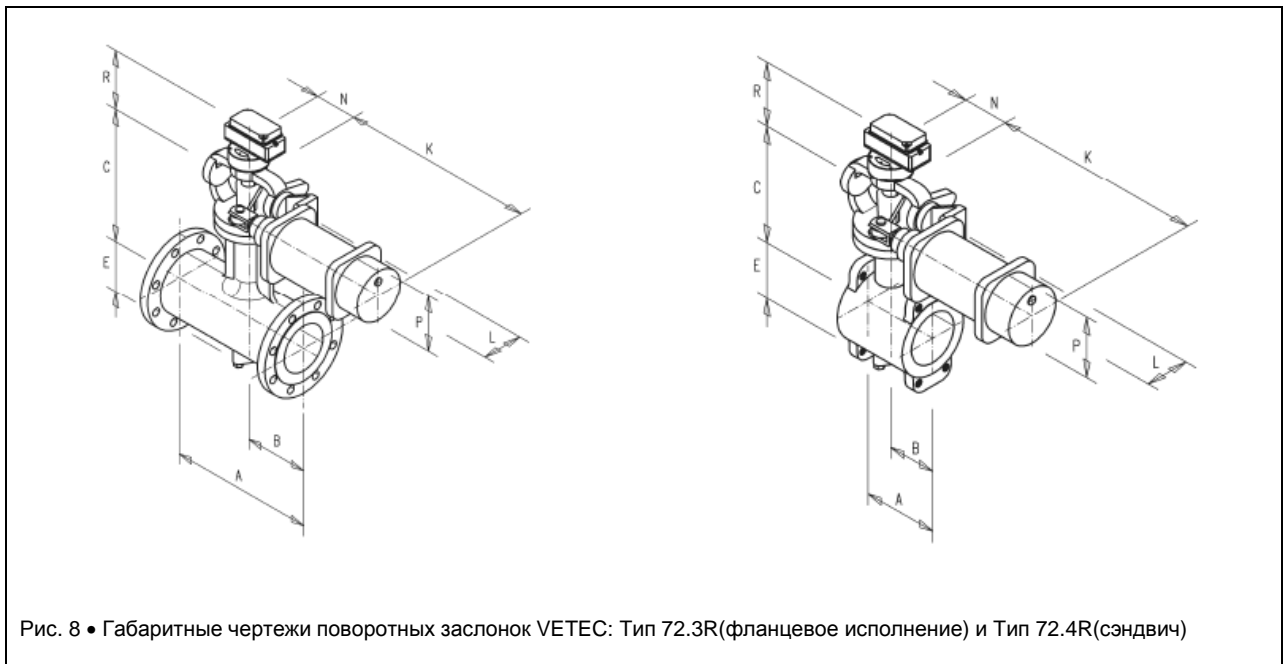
• Габаритные чертежи поворотных заслонок VETEC: Тип 72.3R(фланцевое исполнение) и Тип 72.4R(сэндвич)
